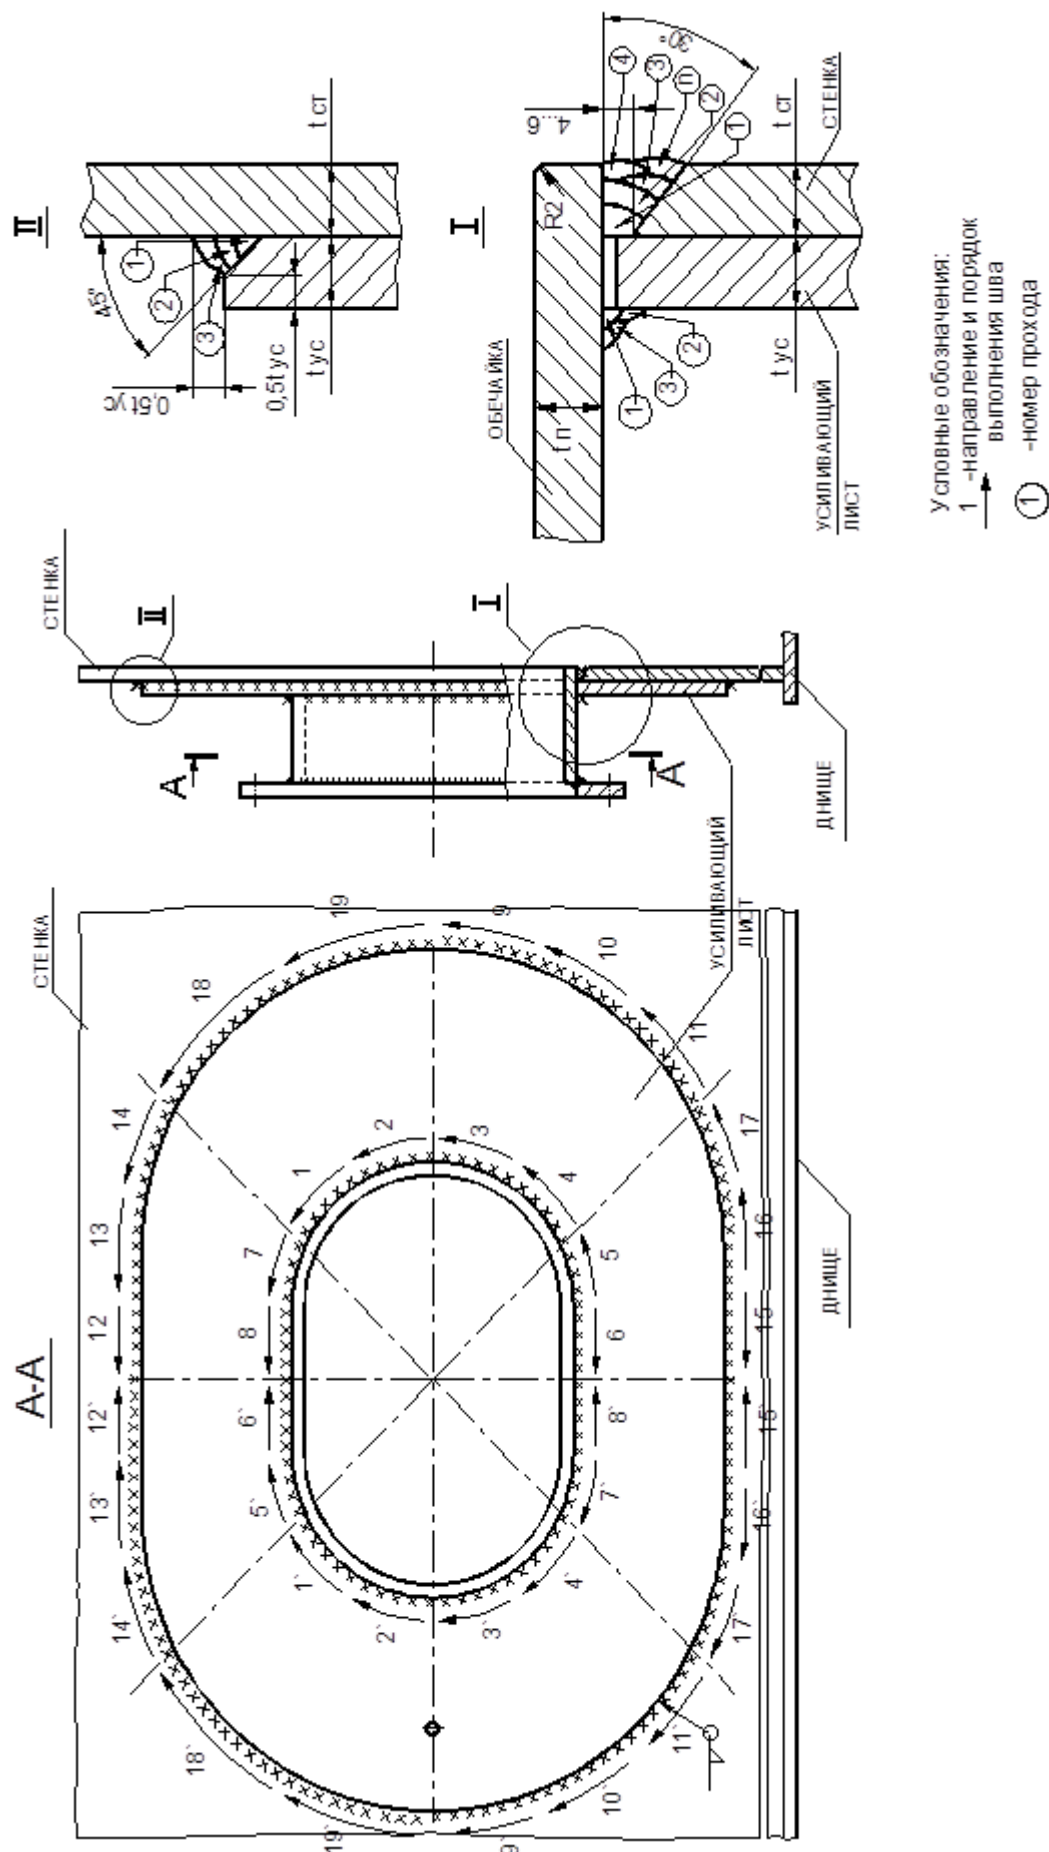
Схема сварки овального люка-лаза в стенке
